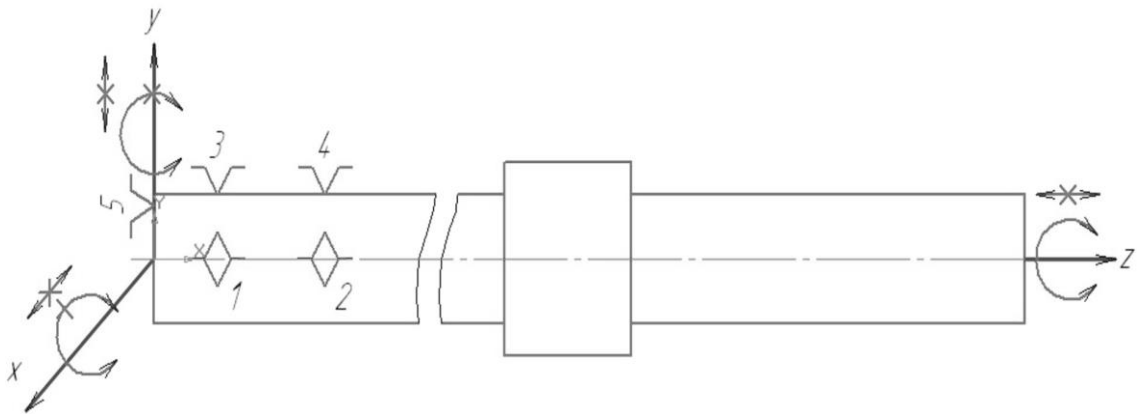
Схема базування заготовки на 020, 025 операції
